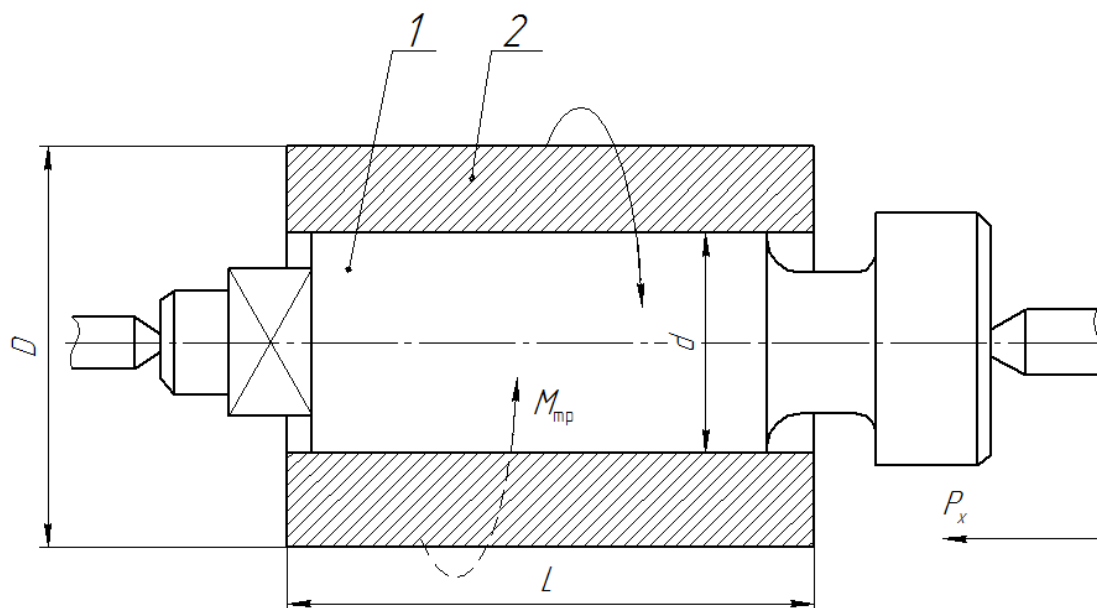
Будова й параметри циліндричної оправки під запресовування: 1 – оправка; 2 – деталь
